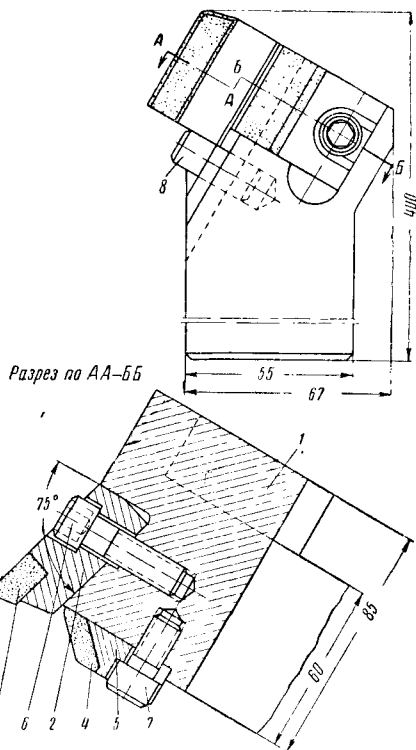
а. Чашечный резец конструкции ВНИИ с механическим креплением пластинки твёрдого сплава силами резания: 1—державка; 2—режущая пластинка твёрдого сплава; 3—стружколоматель; 4—стержень; 5—втулка; 6—пружина; 7—втулка разжимная
